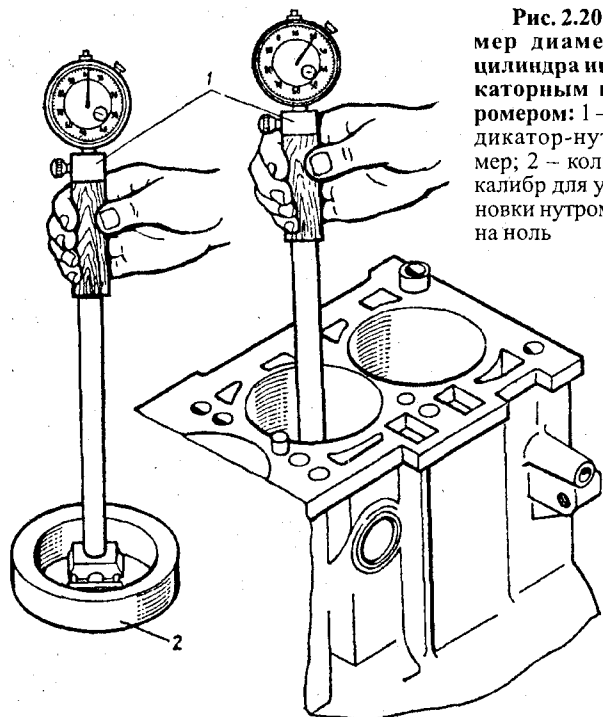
Замер диаметра цилиндра индикаторным нутромером: 1 – индикатор-нутромер; 2 – кольцо-калибр для установки нутромера на ноль
